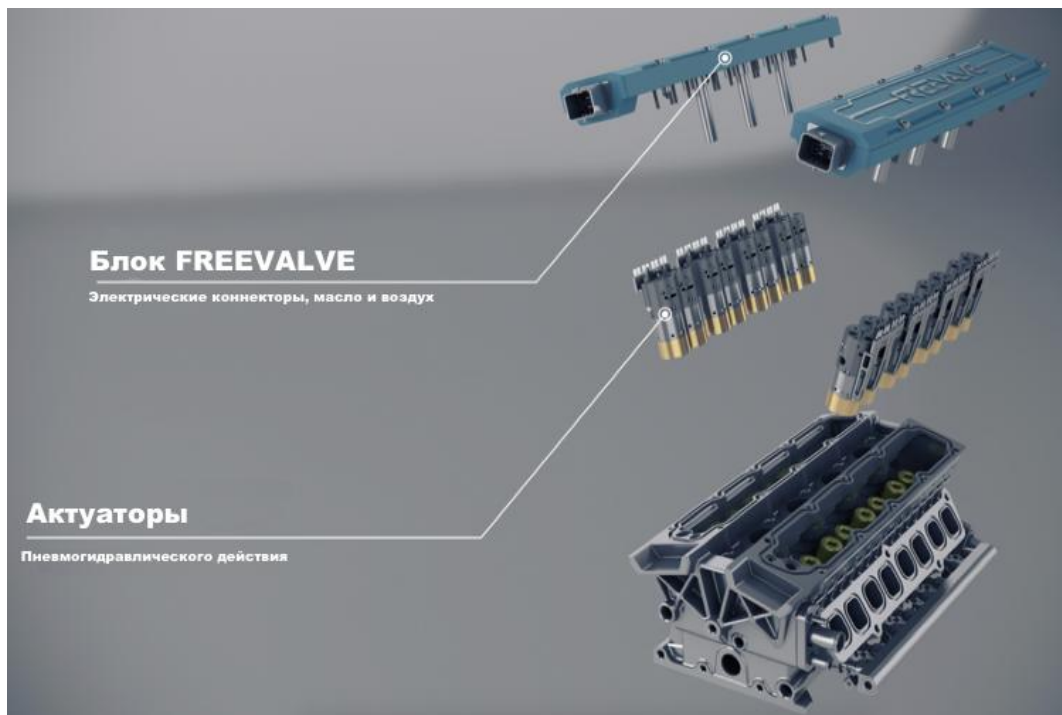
Устройство ГРМ от FreeValve [20]
